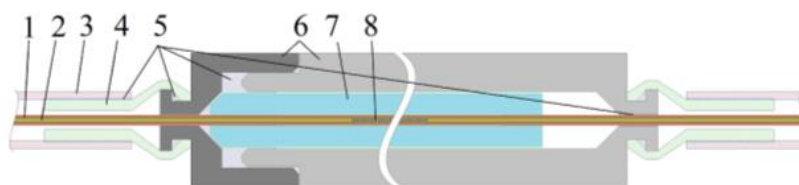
Конструкция датчика со стеклянным капилляром и стальным корпусом
